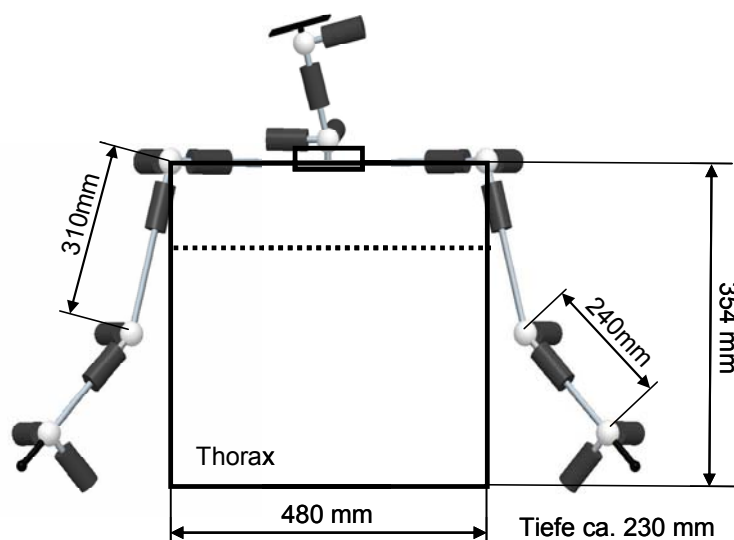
Bauraum im Torso des Roboters für die Anbringung der Arme
